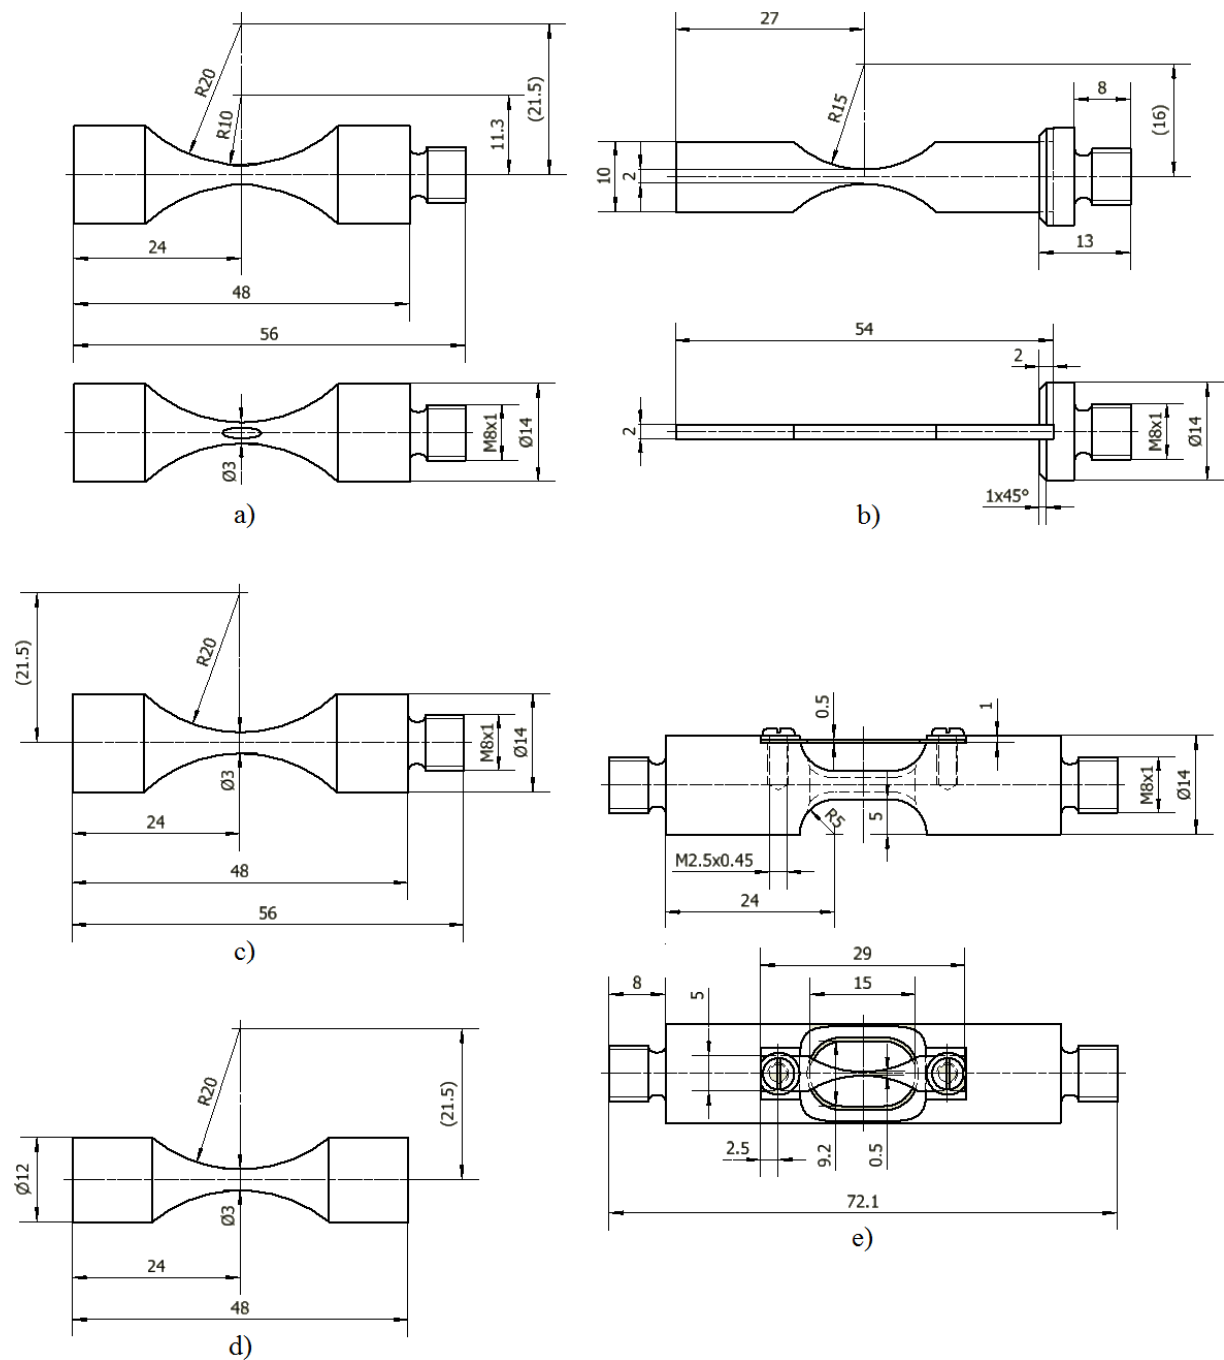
a) Zweiseitig gekerbte Sanduhrprobe für Ultraschall-Ermüdungsprüftechnik, b) Flachprobe für Ultraschall-Ermüdungsprüftechnik, c) ungekerbte Sanduhrprobe für Ultraschall-Ermüdungsprüftechnik, d) Sanduhrprobe für servohydraulische Ermüdungsprüftechnik und e) Miniaturproben-Träger-System für Ultraschall-Ermüdungsprüftechnik
